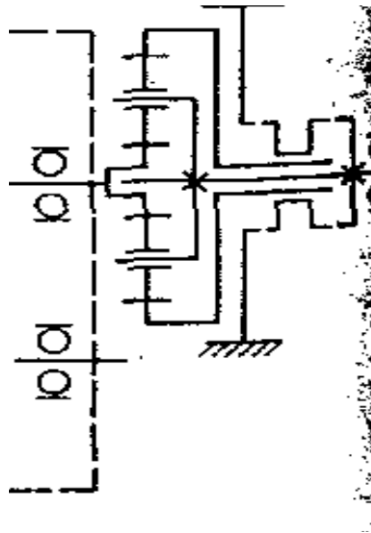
Задний планетарный редуктор, устанавливаемый в сборе с КП грузового автомобиля МАЗ-5336
